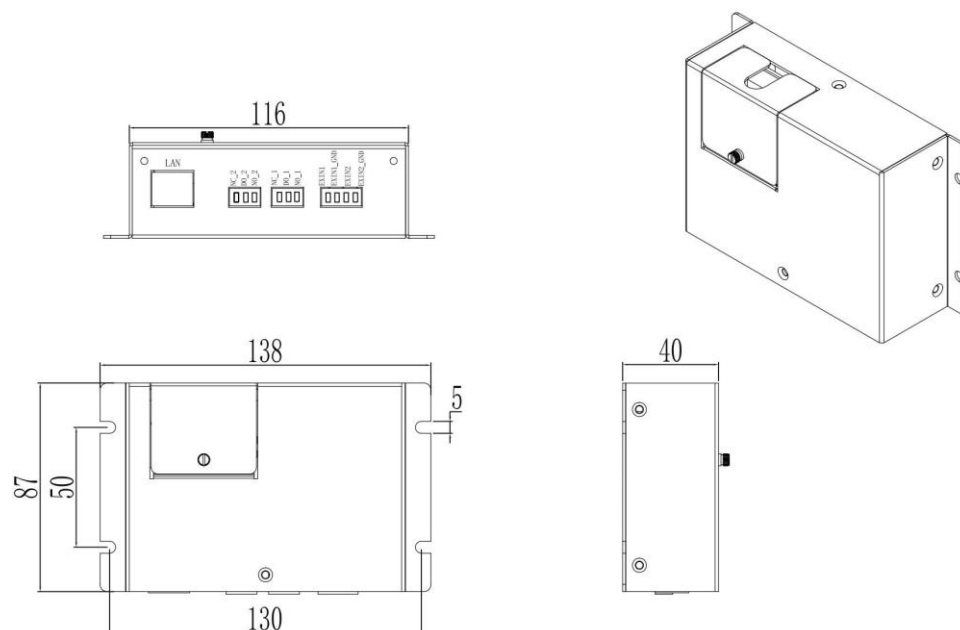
Dimensiones de la Pizarra de Contacto Seco
